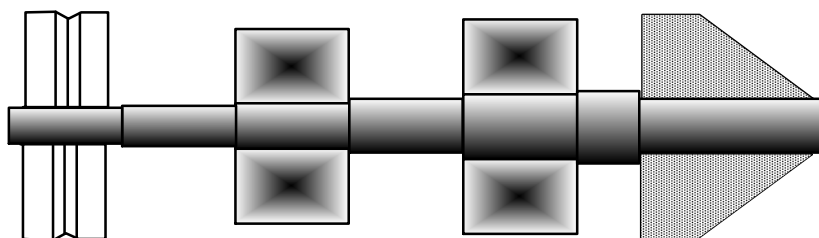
Схема вала с подшипниками, устанавливаемыми с одной стороны.
